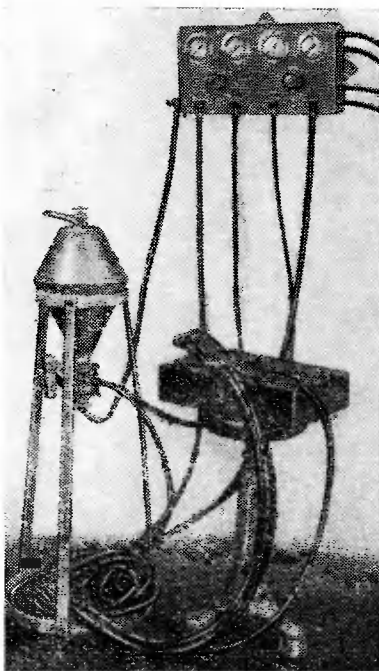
Установка «Шори» (Англия) для газопламенного напыления покрытий из пластмасс и металлов
